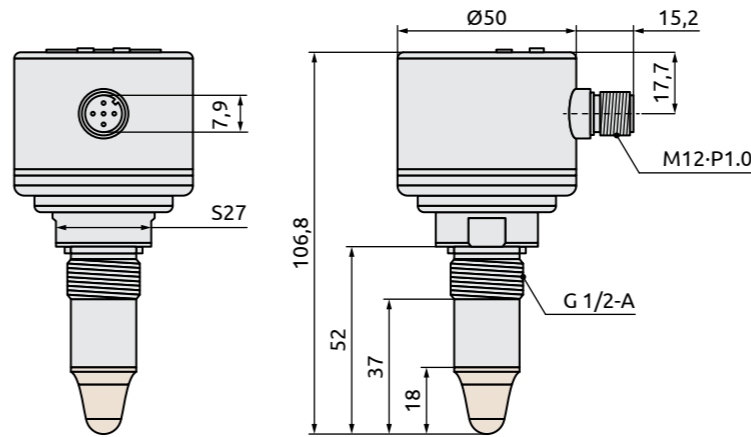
Габаритный чертеж электромагнитного датчика ELS-052-T
